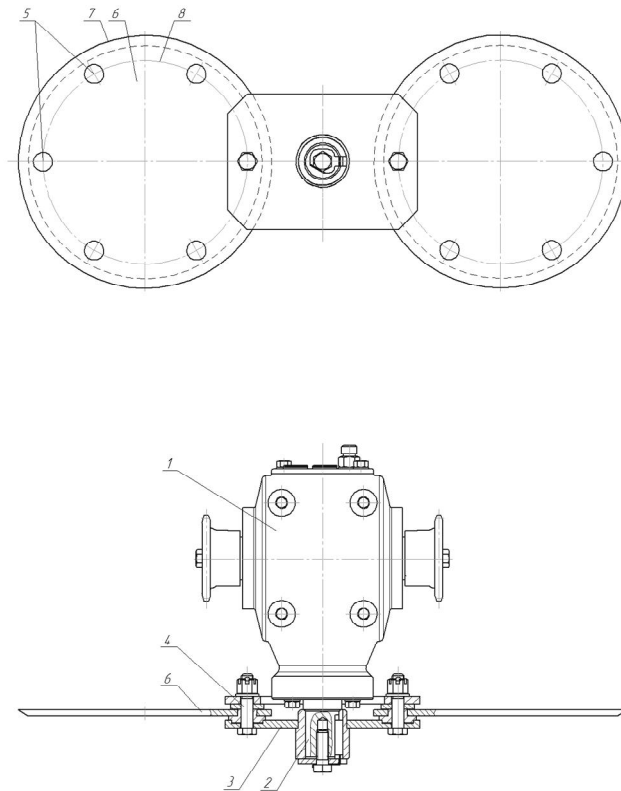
Різальний апарат: 1 – коробка; 2 – вихідний вал; 3 – маточина; 4 – вісь; 5 – отвір; 6 – ніж; 7 – різальна кромка; 8 – коло
